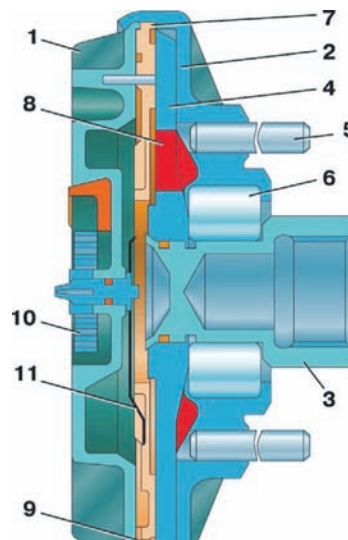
Муфта привода вентилятора: 1 – кришка; 2 – корпус; 3 – вал; 4 – диск ведучий; 5 – шпилька кріплення вентилятора; 6 – підшипник; 7 – компаунд; 8 – рідина по ліметилсилоксанова; 9 – перепускний отвір; 10 – клапан; 11 – бімета лева пружина
